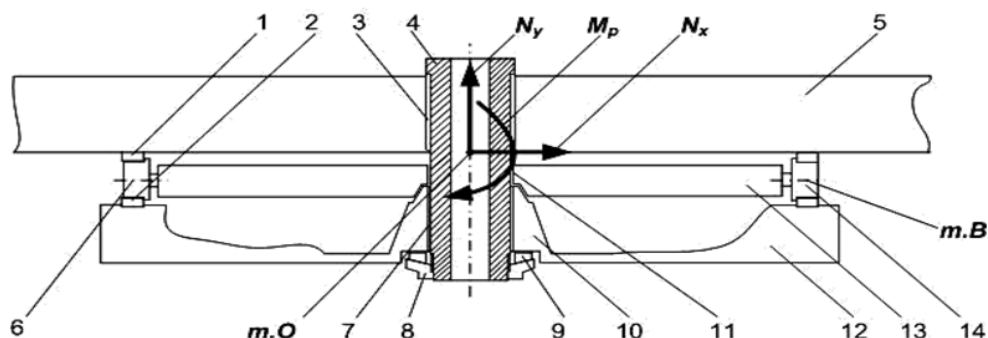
Схема общей конструкции опорно-поворотного устройства и расположения реакций связей: 1 – верхний рельс, 2 – нижний рельс, 3 – втулка (верхний и нижний пояса) поворотной платформы, 4 – центральная цапфа, 5 – поворотная платформа, 6 – роликовый круг, 7 – втулка нижней рамы, 8 – гайка центральной цапфы, 9 – сферическая шайба, 10 – отливка нижней рамы, 11 – втулка сепаратора роликового круга, 12 – нижняя рама, 13 – сепаратор роликового круга, 14 – передний ролик (точка В), N_x – горизонтальная составляющая нагрузок, N_y – вертикальная составляющая нагрузок, M_p – реактивный (изгибающий) момент.
